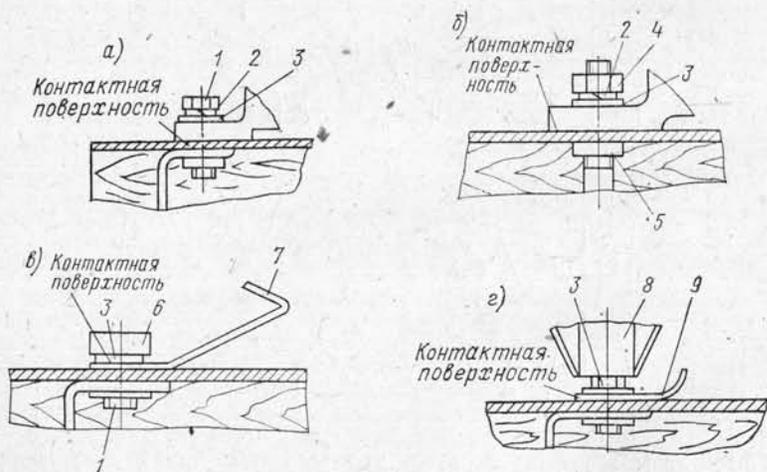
Узлы крепления и заземления корпусов на перегородках с металлической обшивкой: а, б — неамортизированных; в — с амортизатором типа АКПО; г — с амортизатором типа А1 или А2.
